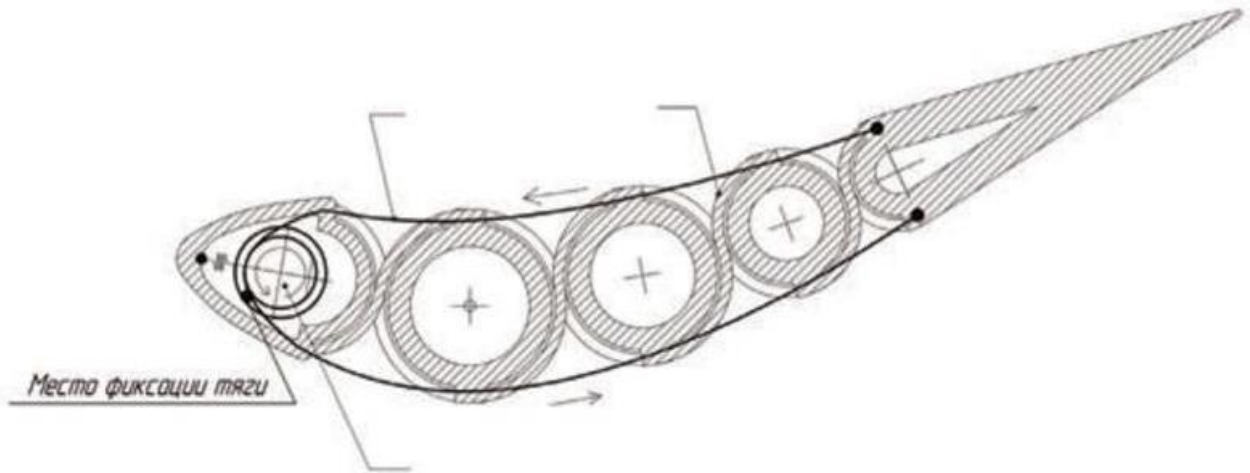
Конструктивна схема мехатронного вузла адаптивного крила: 1 - електромеханічний привід; 2 - тяга; 3 - циліндричний шарнір подвійної дії.
